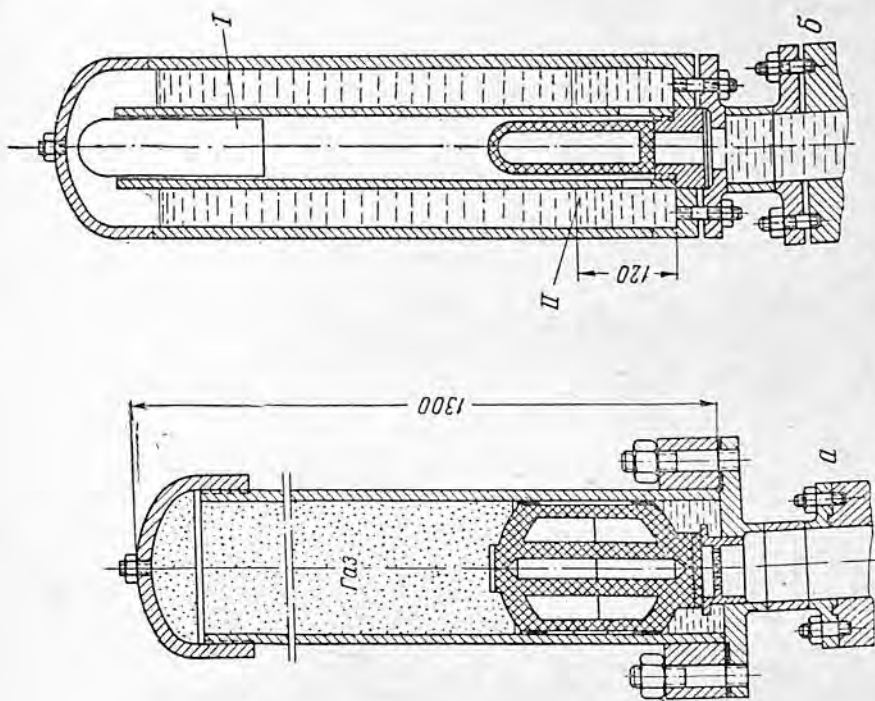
Воздушные клапаны поплавкового типа конструкции ГрозНИИ.
